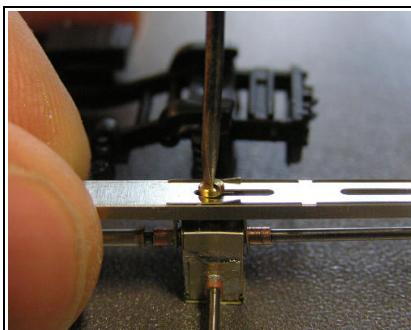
Die Starrachse im Chassisblech mit der Schraube M1x2 befestigen und gewünschten Achsabstand einstellen.
